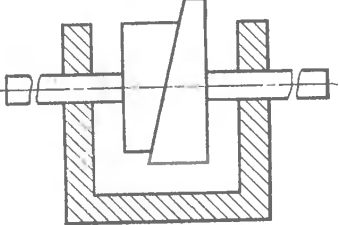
Приспособления для проверки точности сборки под сварку:
